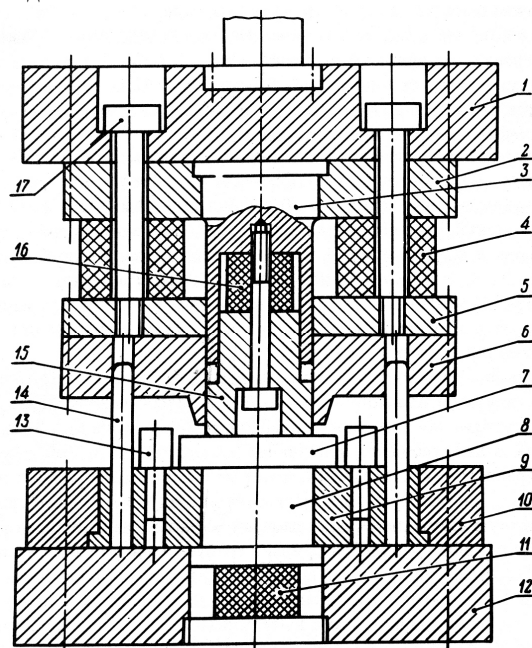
Схема штампа для чистовой вырубки тонколистовых биметаллов
